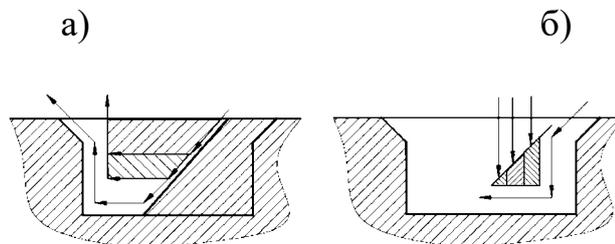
Типовые схемы обработки широких канавок: а) Траектория движения проходного контурного резца; б) Траектория движения прорезного резца
